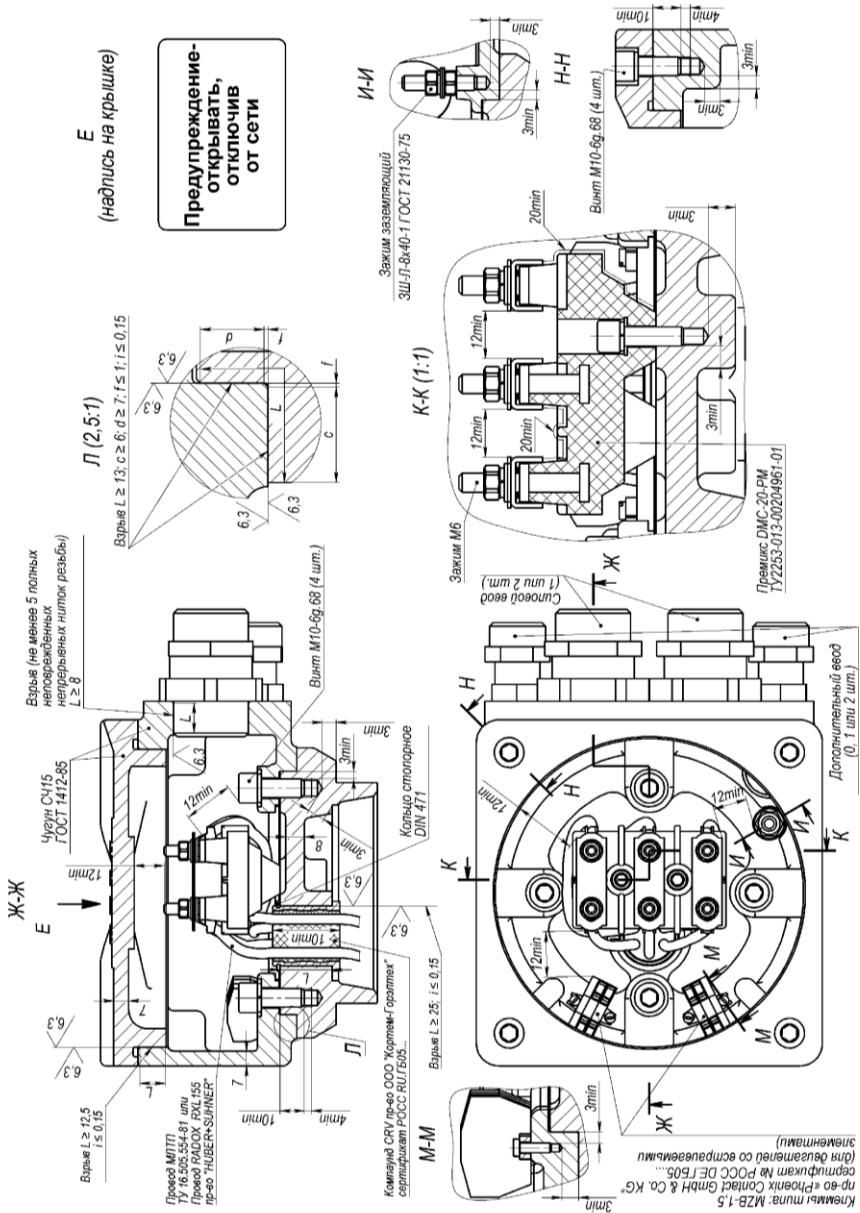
Чертеж взрывозащиты коробки выводов «д»
